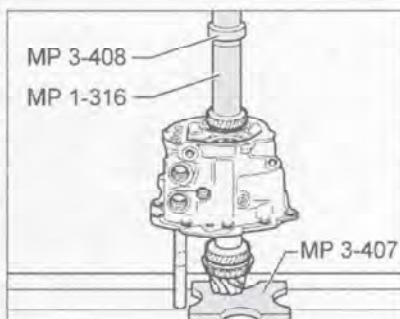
Нагрев шестернию 6-й передачи до 100°C, установите ее на вал. Напрессуйте шестернию на вал с помощью приспособления MP 1-316.
